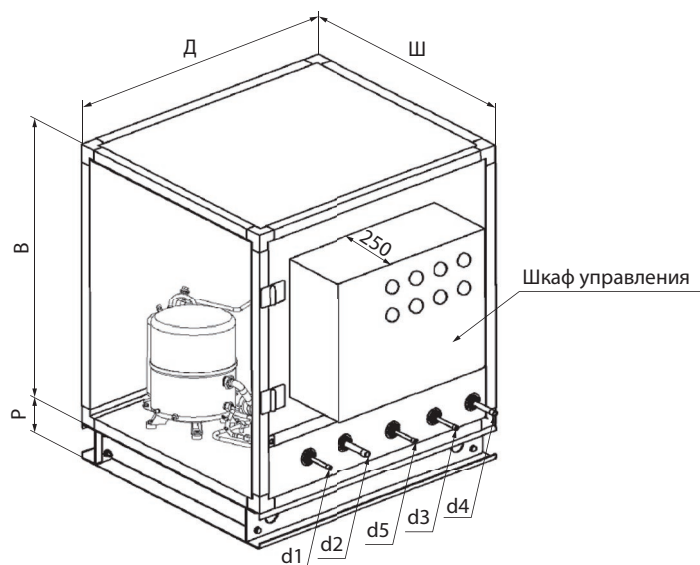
Агрегаты компрессорные типа КРАБ
